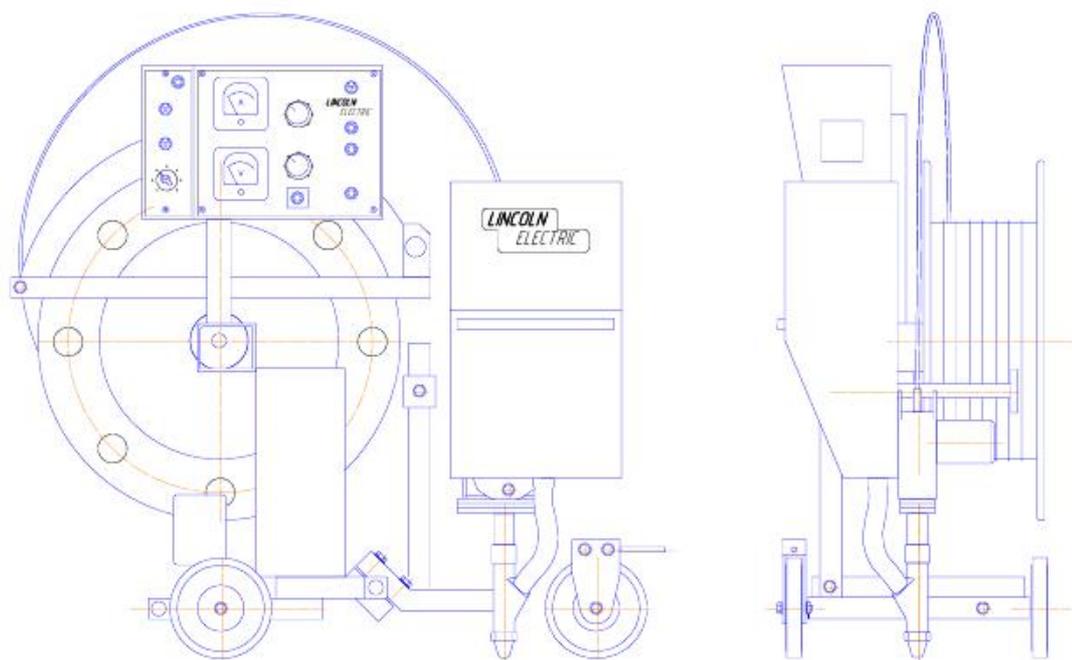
Сварочный трактор LT-7 Lincoln Electric
